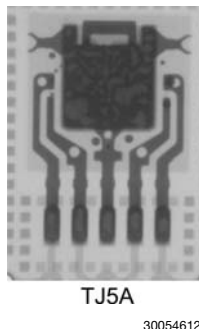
采用 TJ5A PCB 布局模板的 TO-263 THIN 和标准 TO-263 封装
